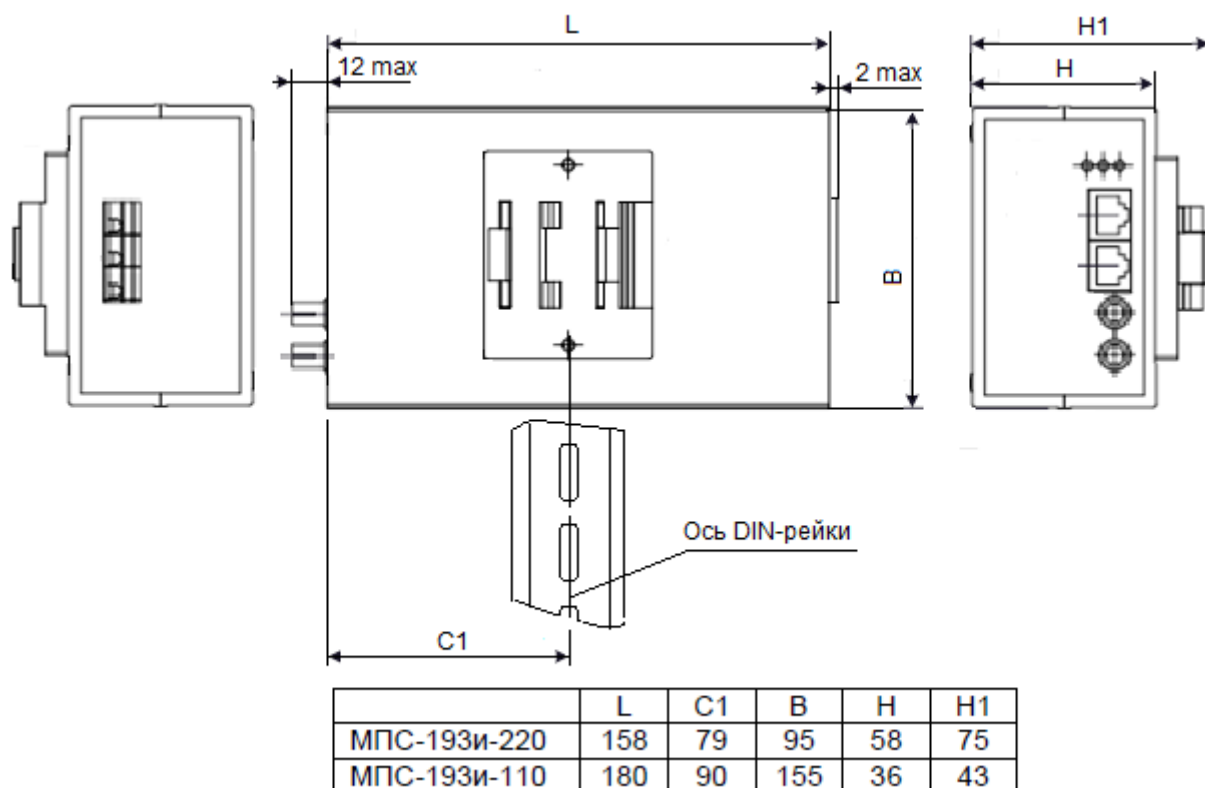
Габаритные и присоединительные размеры МПС-193и-220(110) с поперечным расположением DIN-рейки
